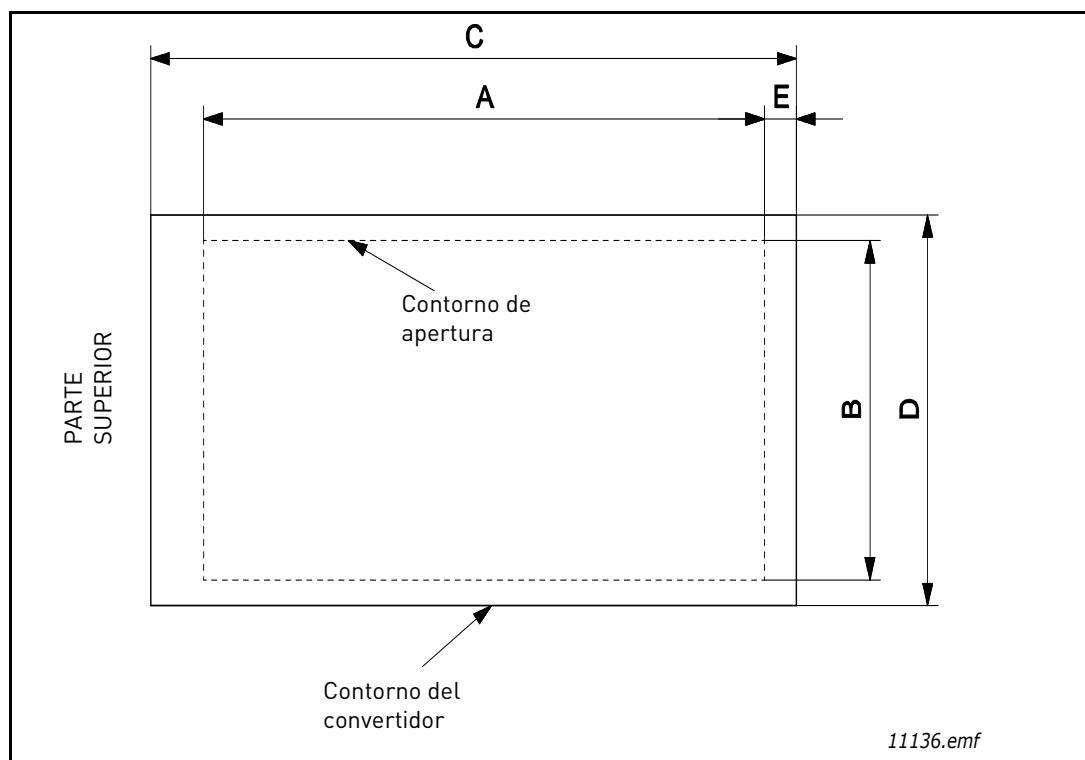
Dimensiones de corte del montaje con bridas de MR4 a MR9
